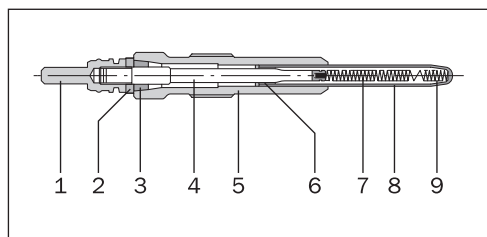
Свеча накаливания закрытого типа: 1 — наконечник; 2 — изолирующая прокладка; 3 — двойное уплотнение; 4 — стержень; 5 — корпус; 6 — уплотнение защитной оболочки; 7 — нагревательная спираль; 8 — трубка; 9 — порошок
